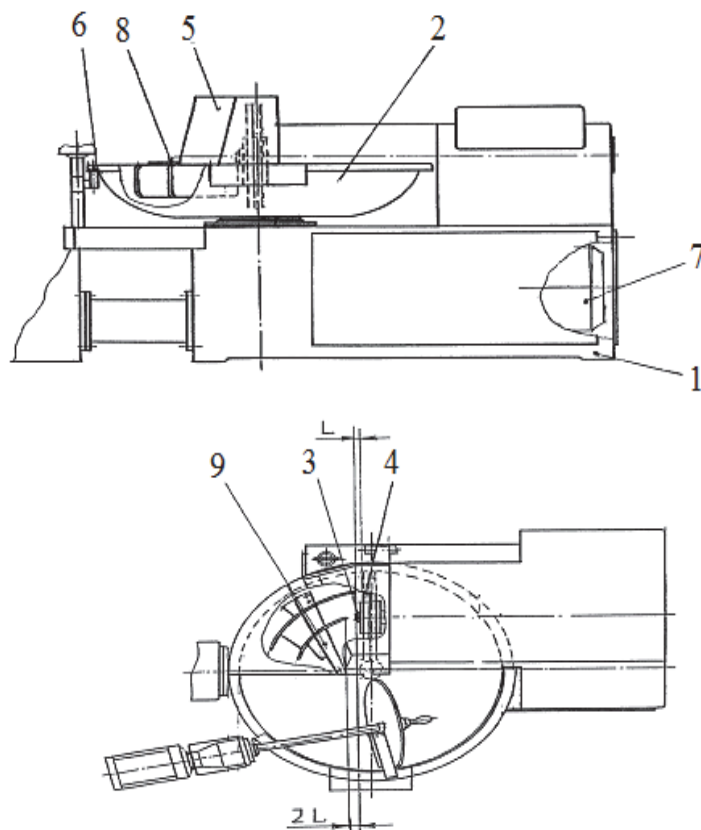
Куттер-прототип [3]: 1 – основание; 2 – чаша; 3 – вал; 4 – ножевыми пакетами; 5 – откидная крышка; 6 – уплотнение; 7 – привод; 8 – горизонтальная полка; 9 – приспособление для рассекания и подавления турбулентности потока жидкого фарша
